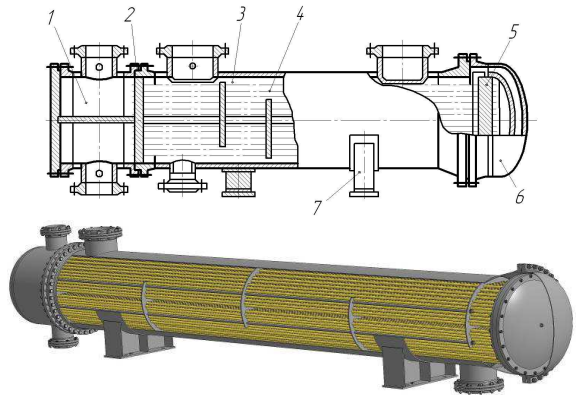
Кожухотрубний горизонтальний багатоходовий конденсатор із плаваючою головкою (КП) з рознімною камерою і плоским днищем: 1 – камера розподільна; 2 – трубна ґратка; 3 – корпус; 4 – трубчатка; 5 – плаваюча головка; 6 – кришка; 7 – опора
